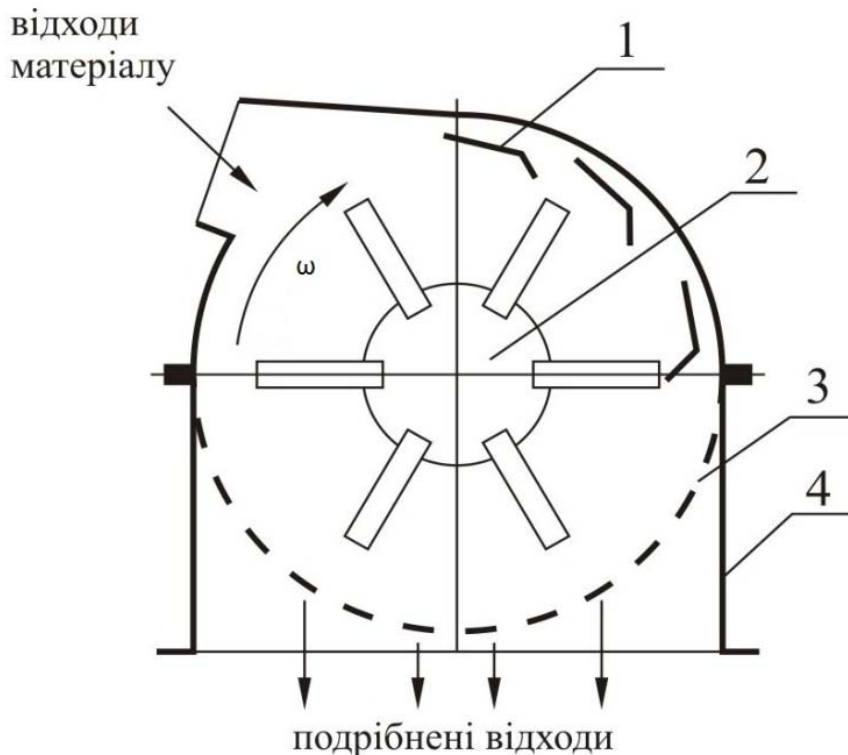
Роторний подрібнювач: 1 - відбивні рифлі; 2 – ротор;
